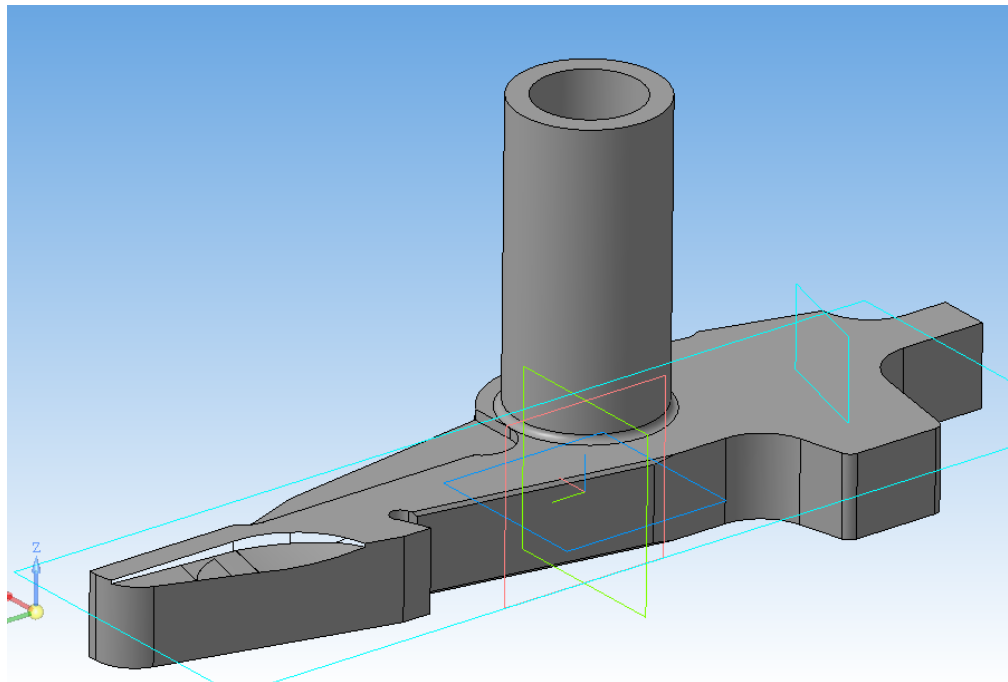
3D модель детали «Экстрактор верхний»
